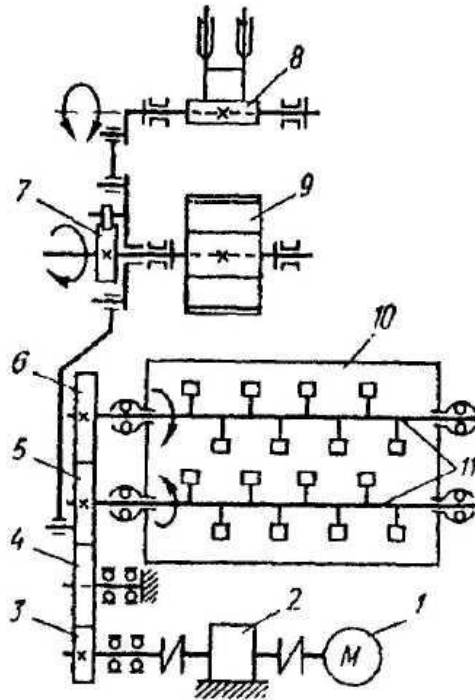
Кінематична схема тістомісильної машини И8-ХТА-12/1: 1 – електродвигун; 2 – редуктор; 3–6 – зубчаті передачі; 7 – храповий механізм; 8 – розпушувач; 9 – роторний дозатор; 10 – місильна камера; 11 – місильні вали
